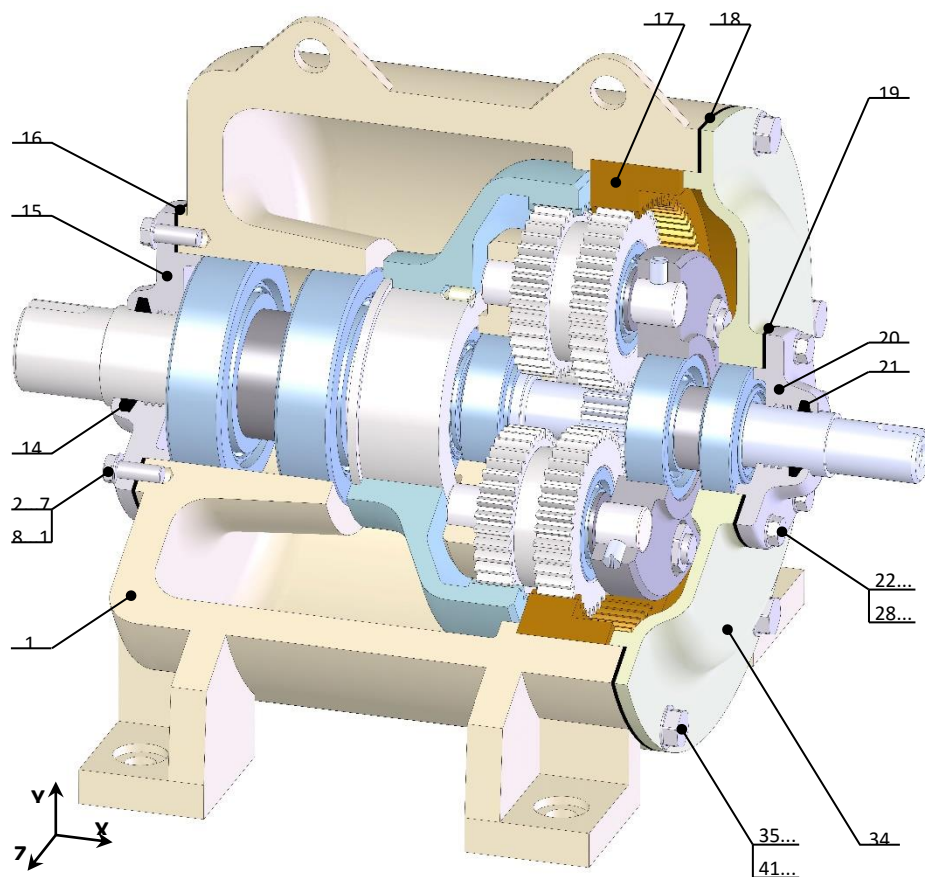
Виріб «Редуктор планетарний двоступінчатий»
